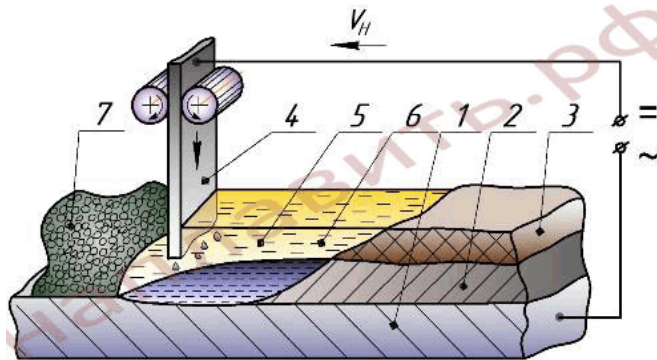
Электрошлаковая наплавка плоской детали лентой: 1 - изделие; 2 - наплавленный металл; 3 - шлаковая корка; 4 - электродная лента; 5 - шлаковая ванна; 6 - металлическая ванна; 7 - сварочный флюс.
